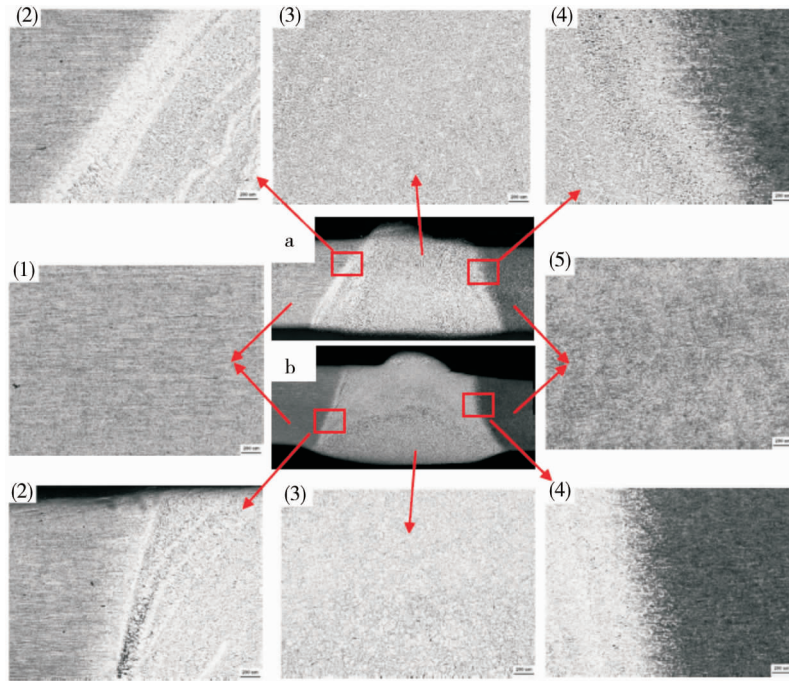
补焊前后 6005A-5083 焊接接头金相组织
